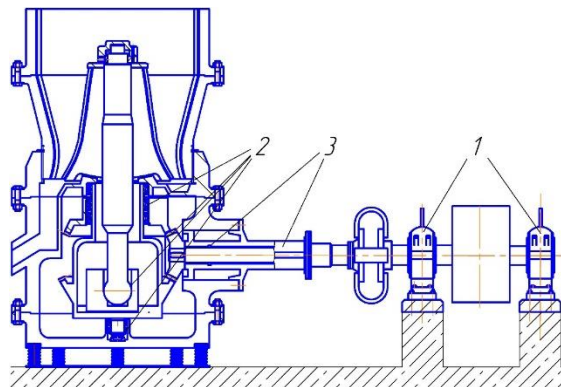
Схема точок змащення конусної дробарки ККД 1500-180: 1 – підшипники електродвигуну; 2 – конічні зубчасті зачеплення, підшипники кочення, сфера на валу; 3 – підшипники ковзання валу привода.
